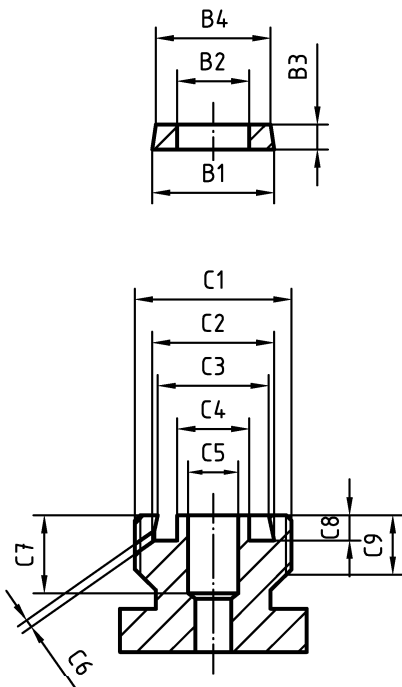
Gewindeanschluss Rp 3/8 L.H.
